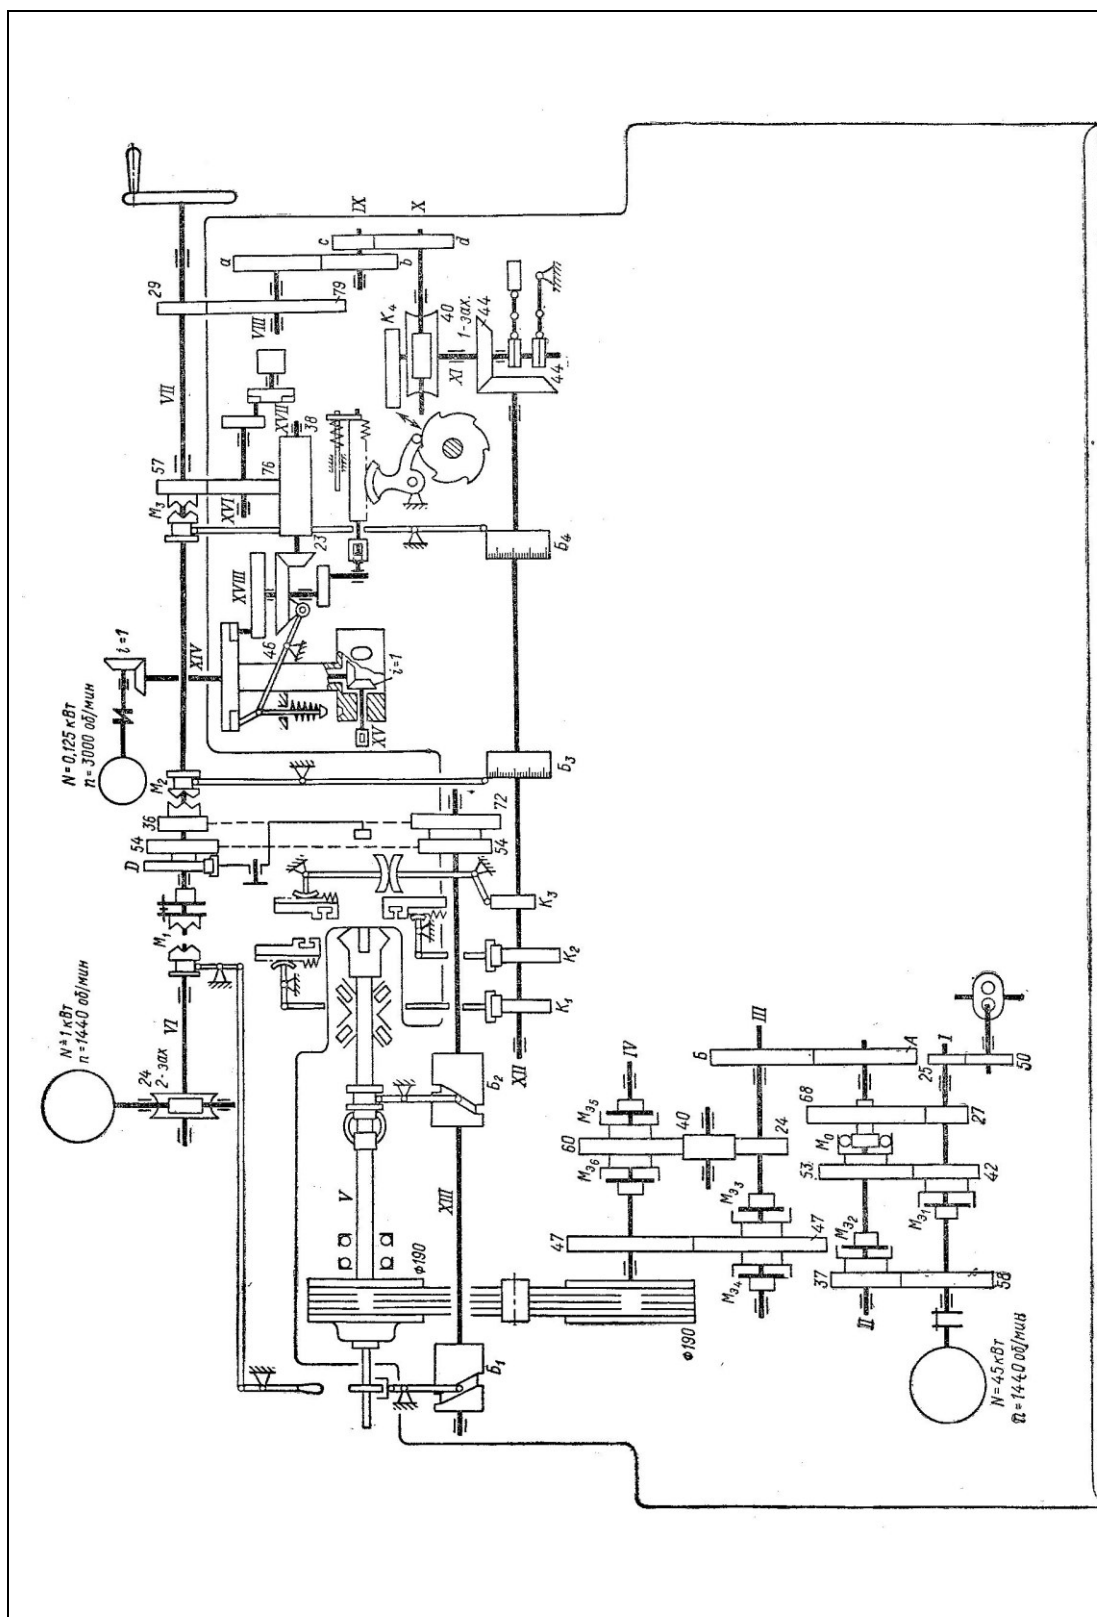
Токарно-револьверный автомат мод. 1Б136
